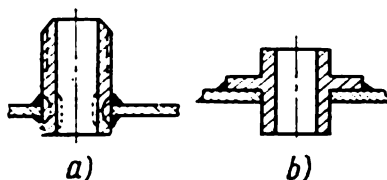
Variantes de la fixation des bagues par soudage
